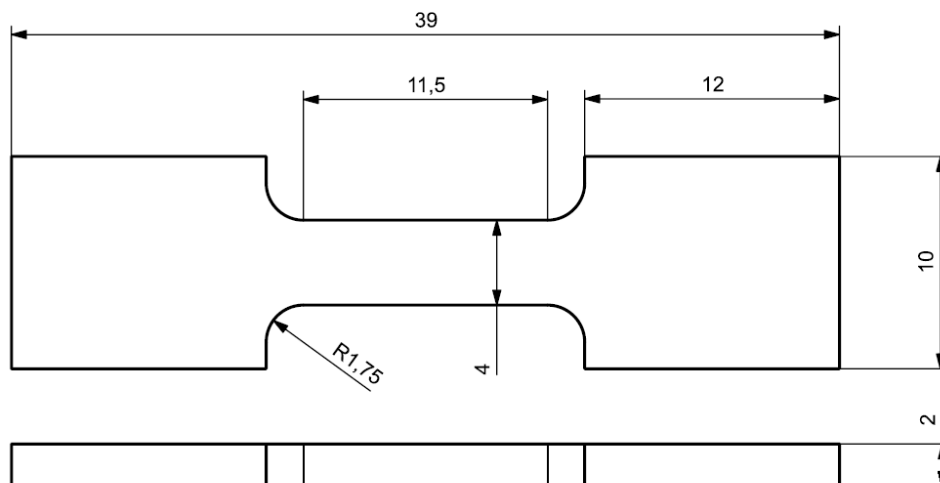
Croqui do corpo de prova utilizado nos ensaios de tração. Dimensões em mm.
